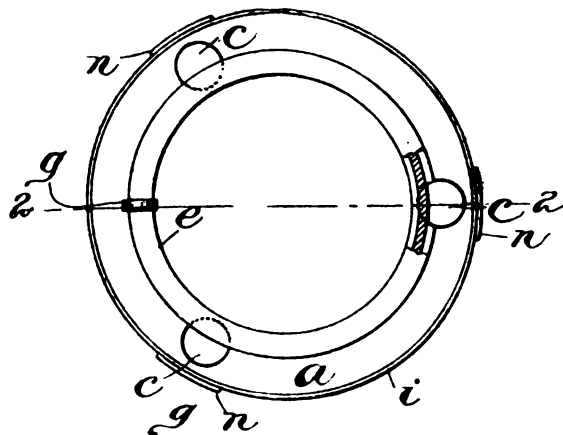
Pianta della disposizione di controllo su cui è montato l'anello.
